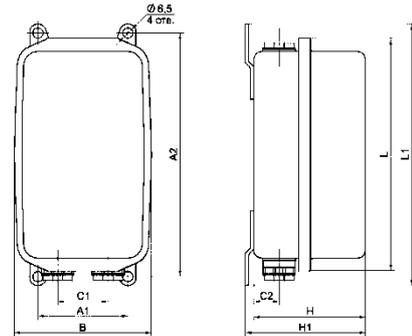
Пускатель ПМ12 100-180А в защитном корпусе. Степень защиты - IP54
